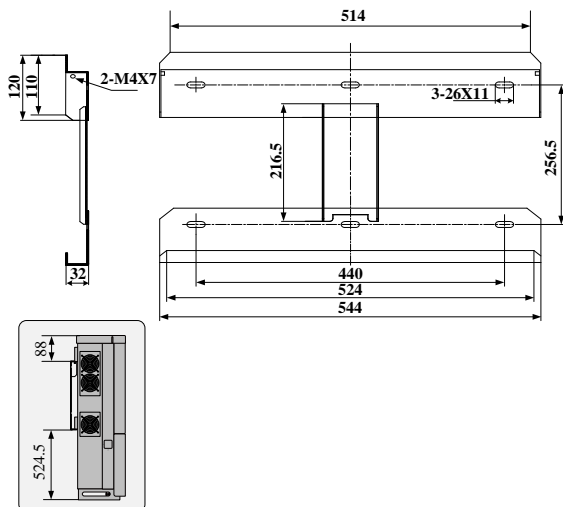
Dimensões da placa traseira (dimensões em mm)
